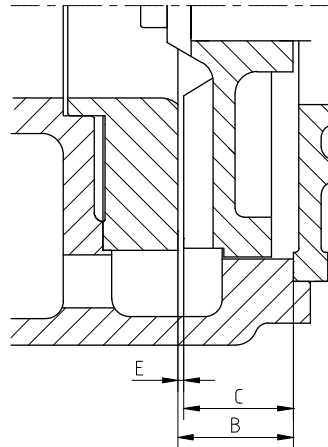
Jocul dintre rotor și placa de uzură, pompe FRE grupa de lagăre 1
